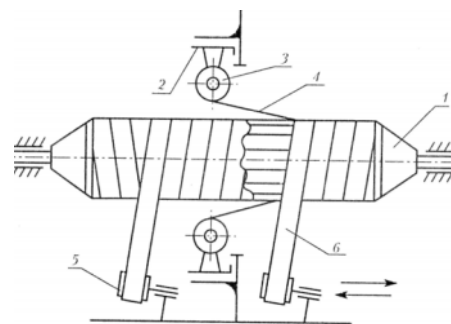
Схема продольно-поперечной намотки: 1 - оправка; 2 - вертлюг; 3 - шпули; 4 - ленты укладки; 5 - поперечные раскладчики; 6 - ленты намотки
